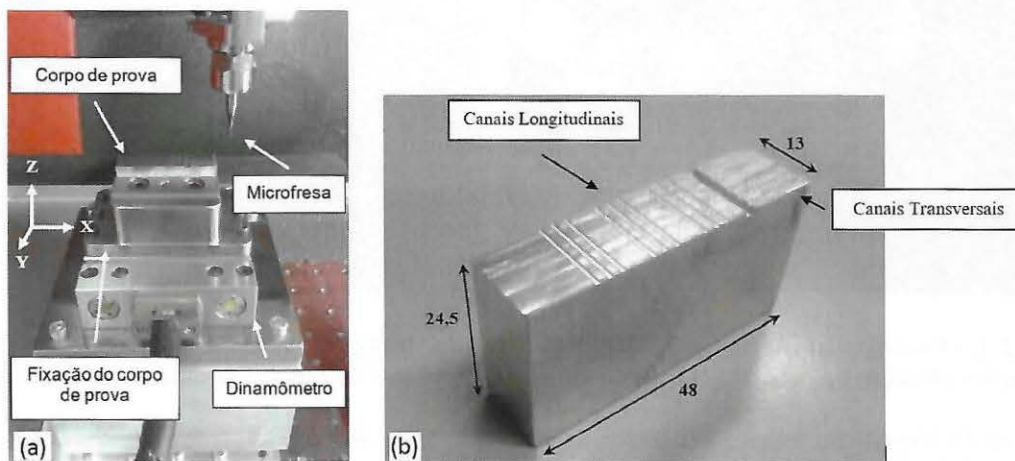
(a) Montagem experimental no centro de usinagem CNC para os ensaios de microfresamento e (b) dimensões dos corpos de prova (mm)
